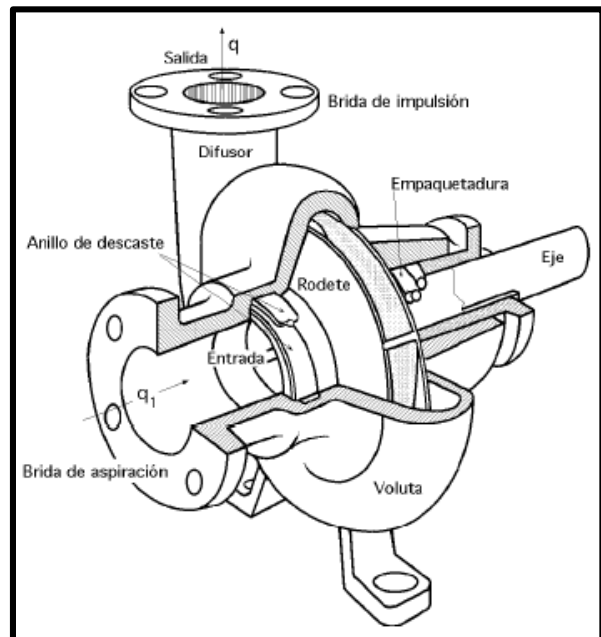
Partes de una Bomba Centrífuga. Fuente: (Fernández, pág. 02)
